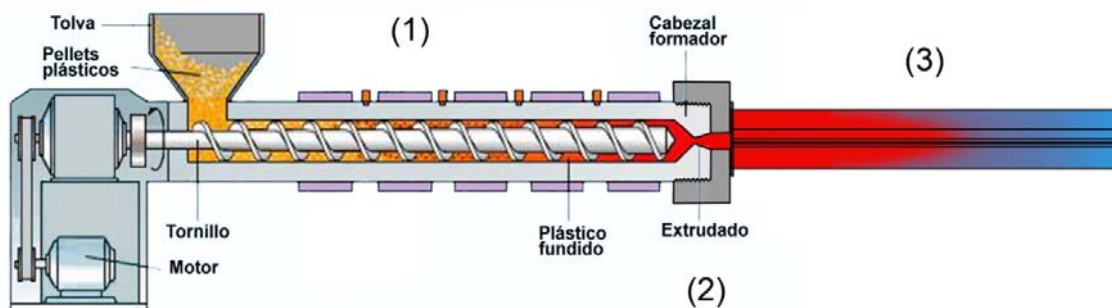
Extrusión modificada; Calentamiento y mezcla (1) Boquilla extrusión (2) Molde de enfriamiento (3).<sup>1</sup>
